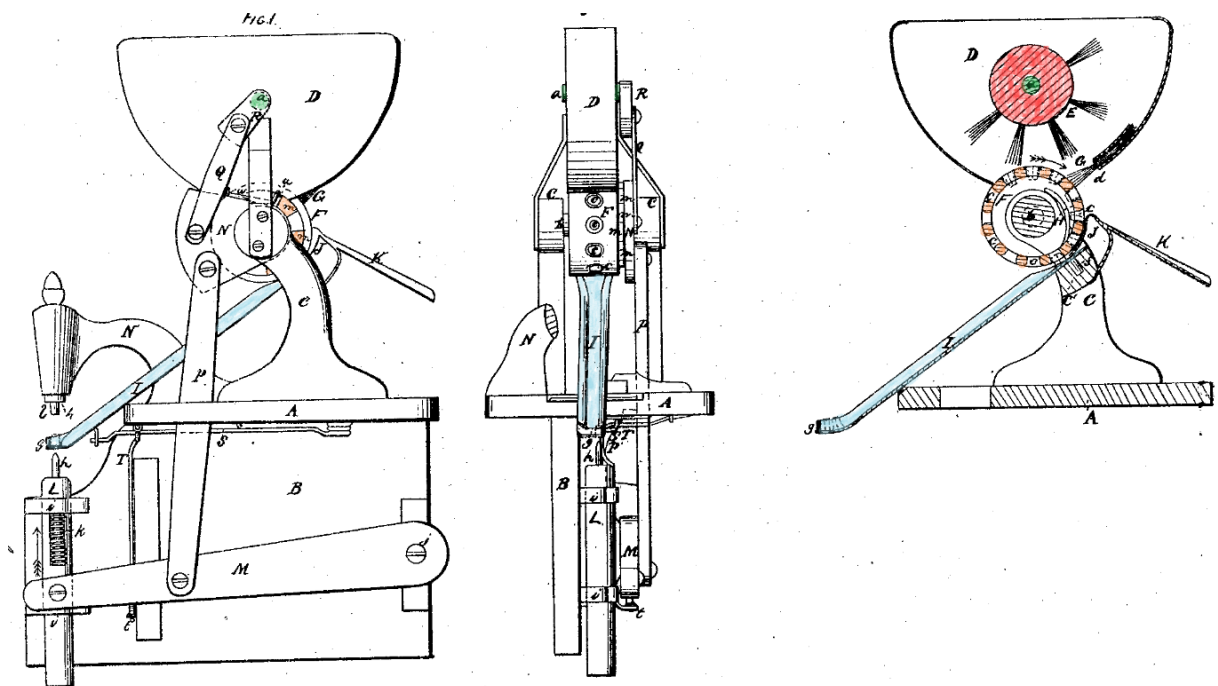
Brevetto No.35952 di T.K.Reed e H.F.Packard del 1862 [9].
